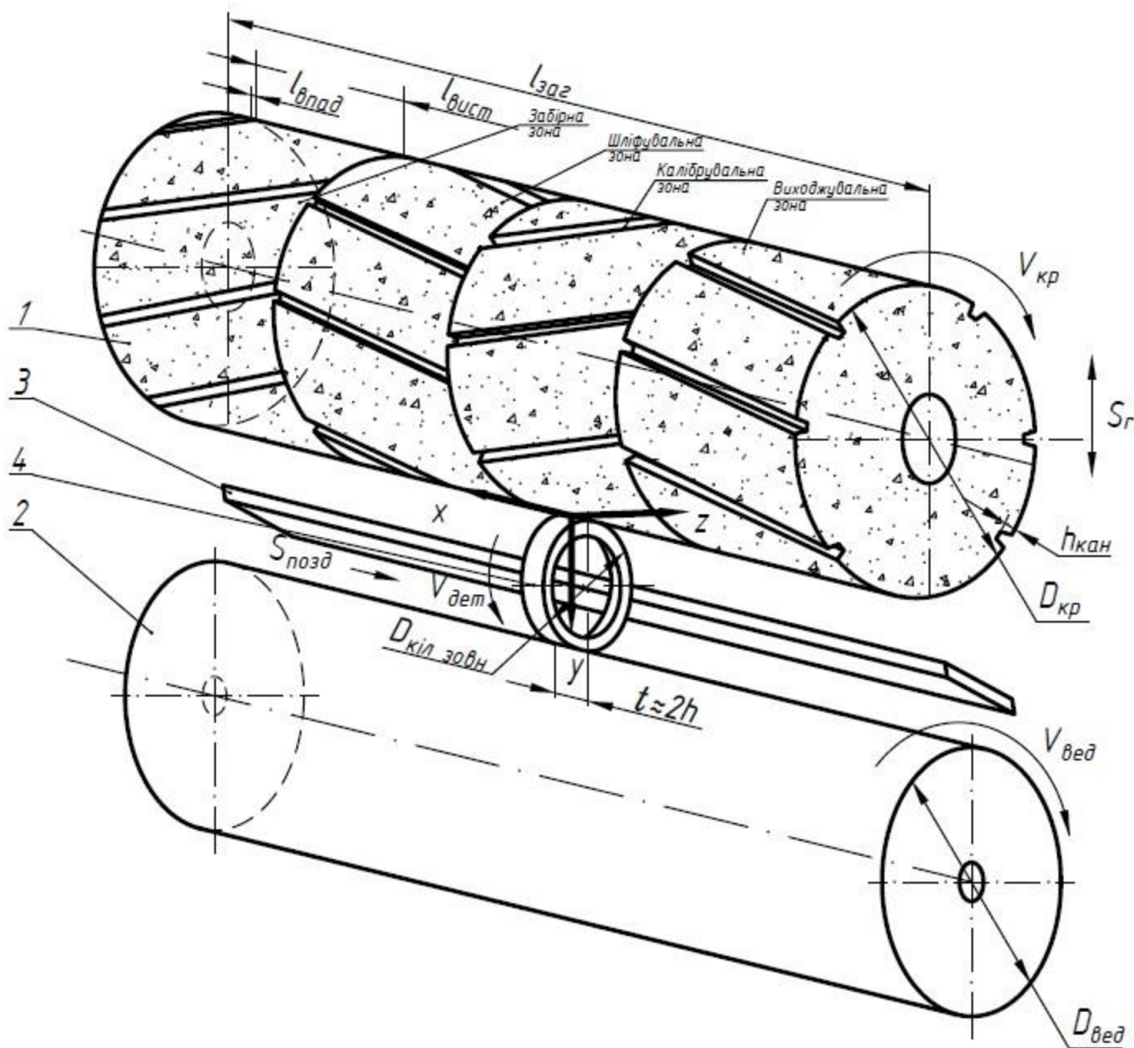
Розрахункова схема утворення нескінченного сегментоподібного теплового джерела: 1 – шліфувальний круг; 2 – ведучий круг; 3 – ніж опорний; 4 – заготовка
